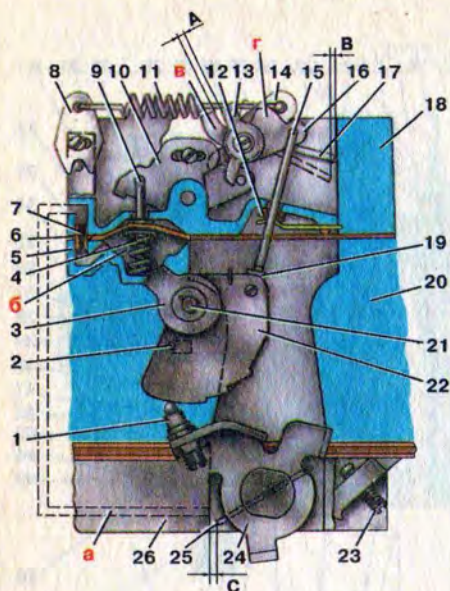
Пусковое устройство: 1 – винт регулировки пускового зазора дроссельной заслонки; 2 – упорный штифт; 3 – рычаг привода воздушной заслонки; 4 – пружина диафрагмы; 5 – крышка диафрагменного механизма; 6 – диафрагма; 7 – жиклер; 8 – рычаг регулировки натяжения оттяжной пружины воздушной заслонки; 9 – шток диафрагмы; 10 – двуплечный рычаг; 11 – оттяжная пружина воздушной заслонки; 12 – уплотнитель; 13 – промежуточный рычаг; 14 – рычаг фиксации воздушной заслонки в крайних положениях; 15 – тяга; 16 – секторный рычаг; 17 – воздушная заслонка; 18 – крышка карбюратора; 19 – муфта регулировки зазора у верхней кромки воздушной заслонки; 20 – корпус карбюратора; 21 – ось системы рычагов; 22 – кулачок; 23 – винт регулировки начального положения дроссельной заслонки; 24 – рычаг управления дроссельной заслонкой; 25 – дроссельная заслонка; 26 – корпус дроссельных заслонок; а – канал подвода управляющего разрежения; б – наддиафрагменная полость; в, г – кромки паза секторного рычага; А – контрольный зазор между рычагами; В – пусковой зазор воздушной заслонки; С – пусковой зазор дроссельной заслонки
